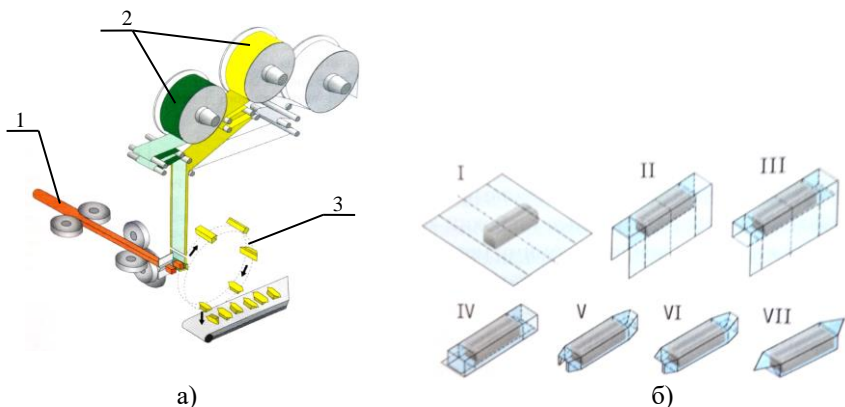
Технологія загортання цукерок “в носок”: а) технологічна схема пакування; б) послідовність загортання; 1 – джгут заготовка; 2 – рулони пакувального матеріалу; 3 – загортувальний ротор.
